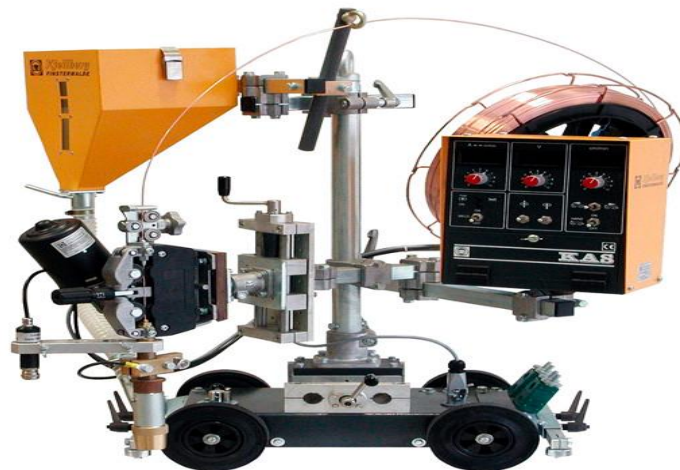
Зварювальний автомат тракторного типу КА 1-ур
